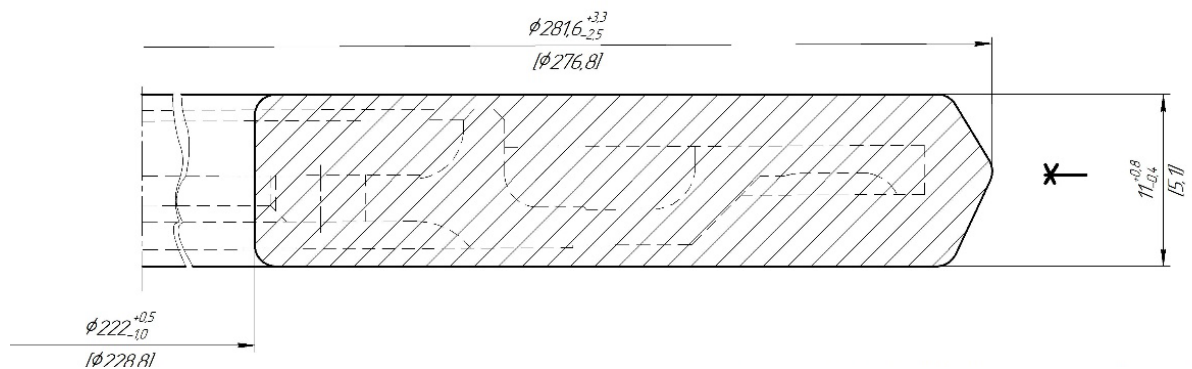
Ескіз заготовки, отриманої методом штампування КГШП
